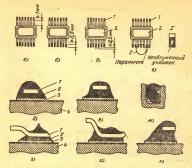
Примеры лужения и пайки выводов планарного корпуса: 1 — вывод; 2 — корпус; 3 — контактивя площадка; 4 — печатная плата; 5 — приной
